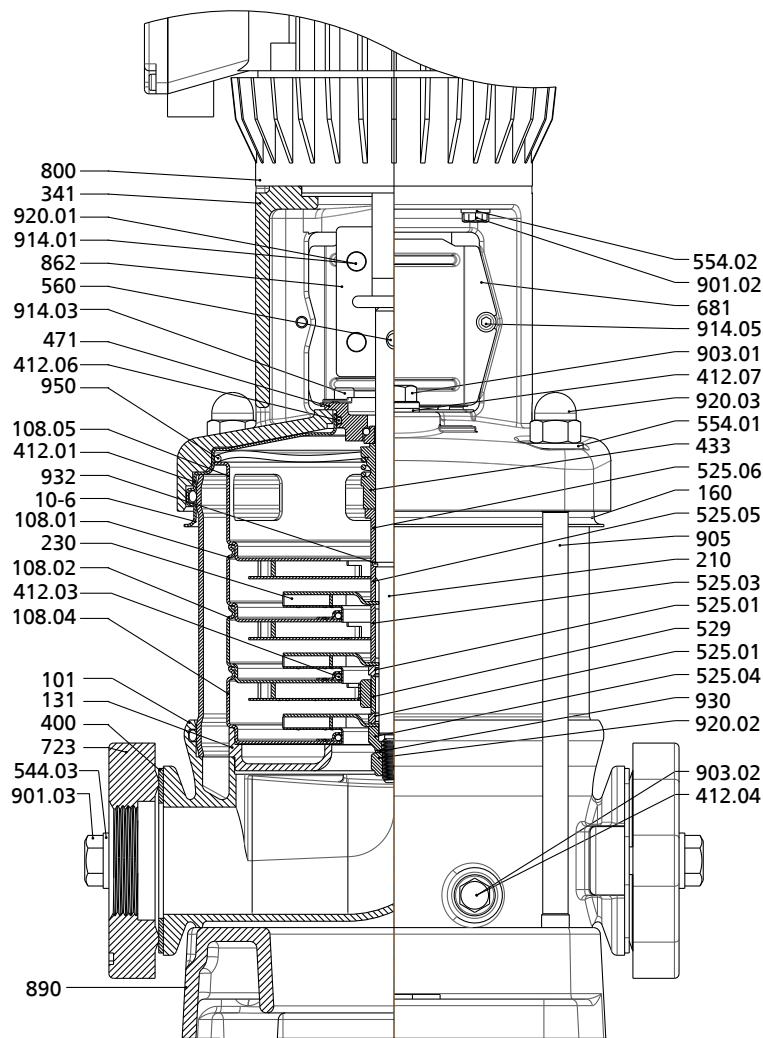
Чертеж общего вида Movitec 10B, 15B
